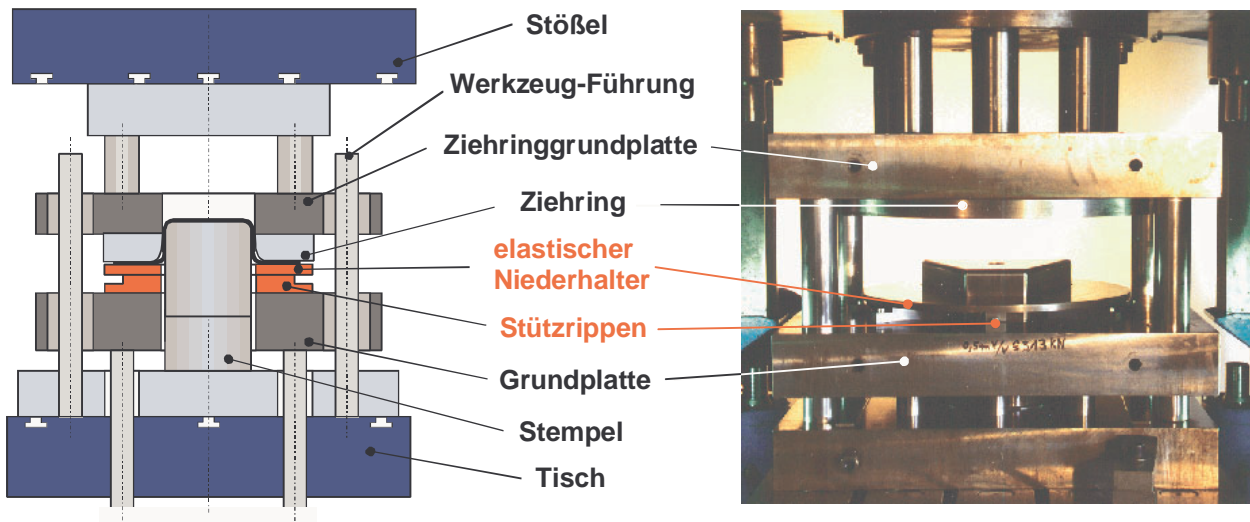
Prinzipieller und realisierter Aufbau des Tiefziehwerkzeugs mit passiv elastischem Niederhalter
